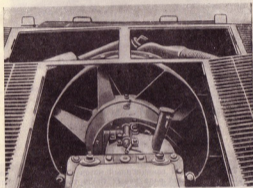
Установка звездообразного мотора Континенталь на колесно-гусеничном танке Т-4.
